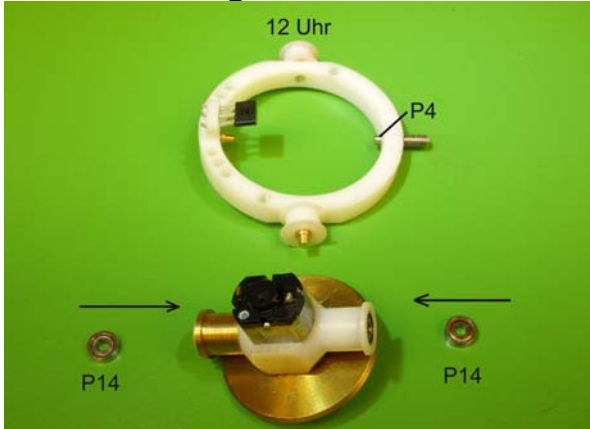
Montage der Kugellager. Kugellager P14 einsetzen, Stiftschraube P4 zurückschrauben.
